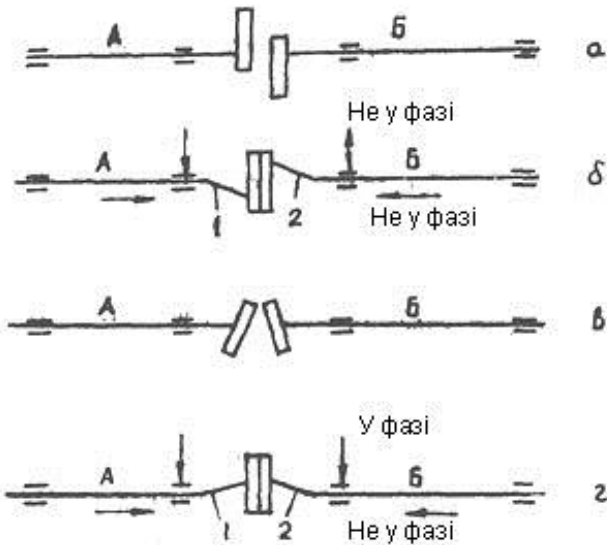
Схема центрування лінії валів за дефектними півмуфтами з поворотом ротора:
